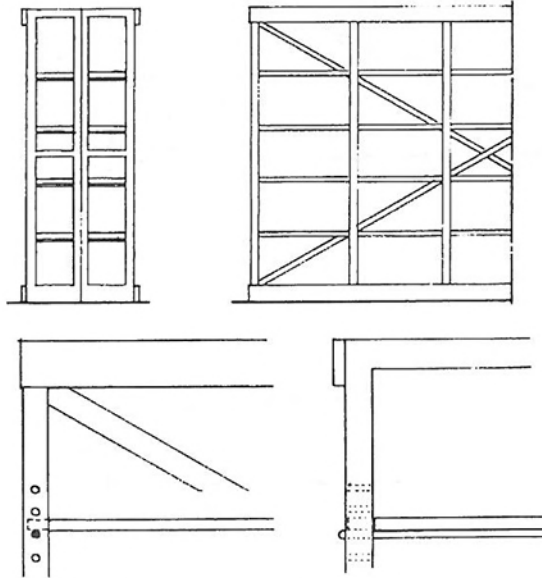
Frente, lado e pormenor da estante para peças de pequenas dimensões
